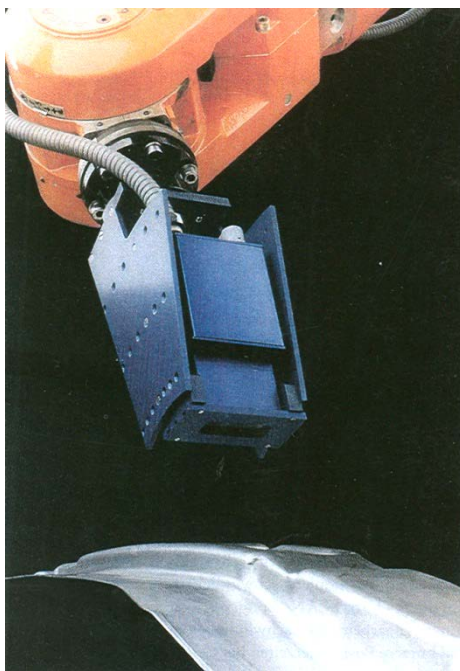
Роботизированный комплекс для лазерной очистки поверхность
